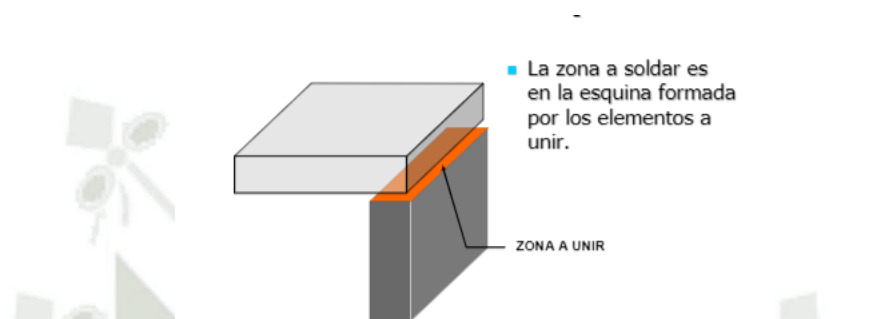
Representación de una soldadura de junta en esquina
